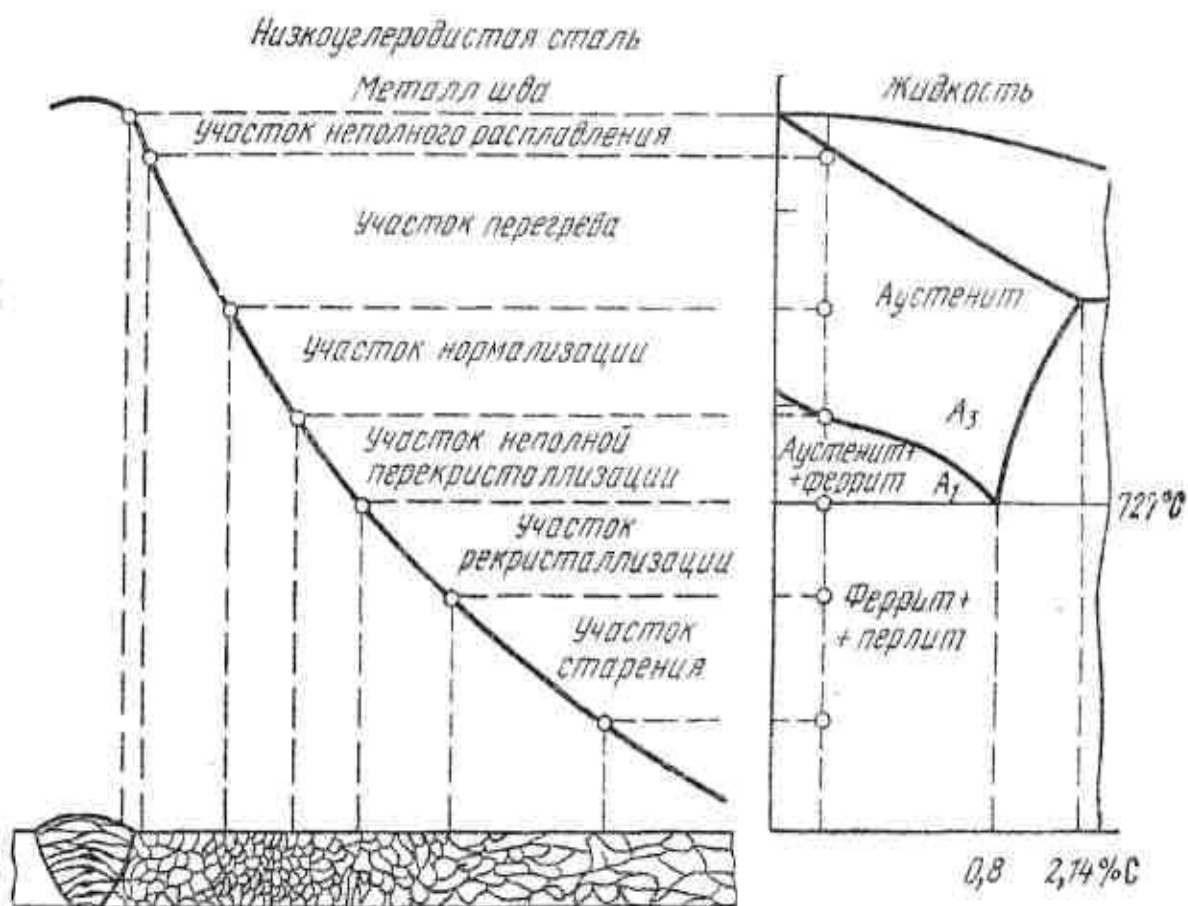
Строение зоны термического влияния сварного шва при дуговой сварке низкоуглеродистой стали
